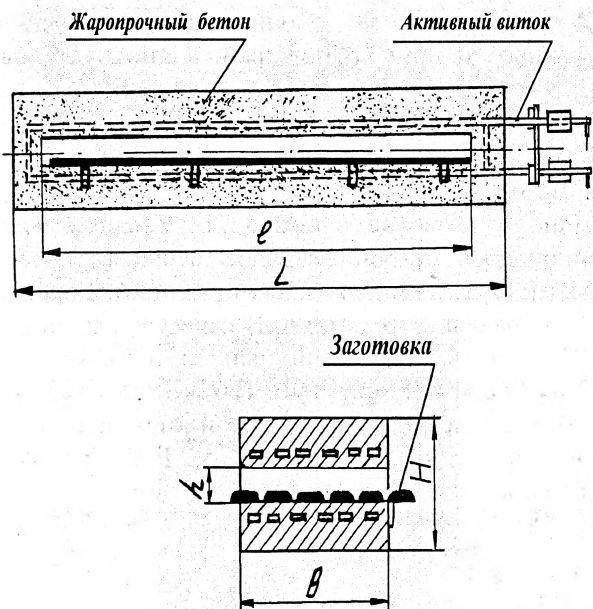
Индуктор для нагрева заготовок рессорных листов под прокатку
